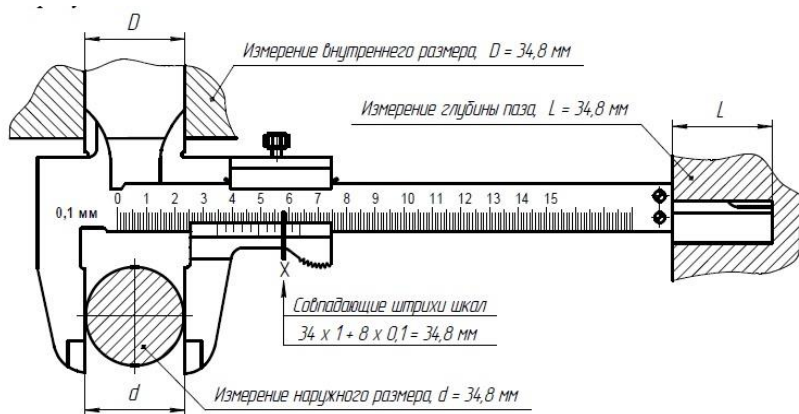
Измерение размеров деталей штангенциркулем типа
